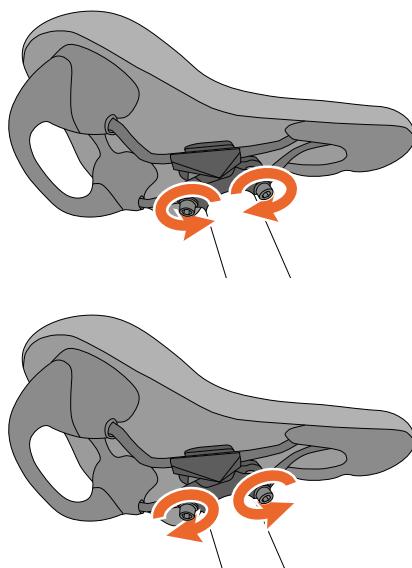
Desserrage des vis de réglage et réglage de position de la selle.
